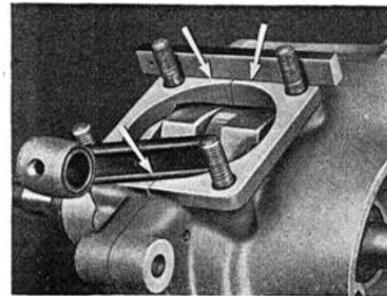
Der Pleuelschaft bzw. die Kurbelwelle müssen symmetrisch zur Gehäusetrennluge liegen (unterer Pfeil). Die Flanschflächen beider Gehäusehälften dürfen nicht gegeneinander versetzt sein; prüfen mit Lineal (obere Pfeile)
